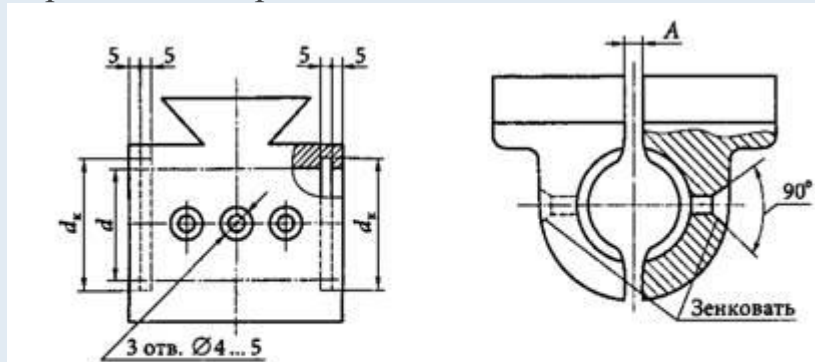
Ремонтный чертеж разъемной (маточной) гайки для ее восстановления заливкой бронзой:
